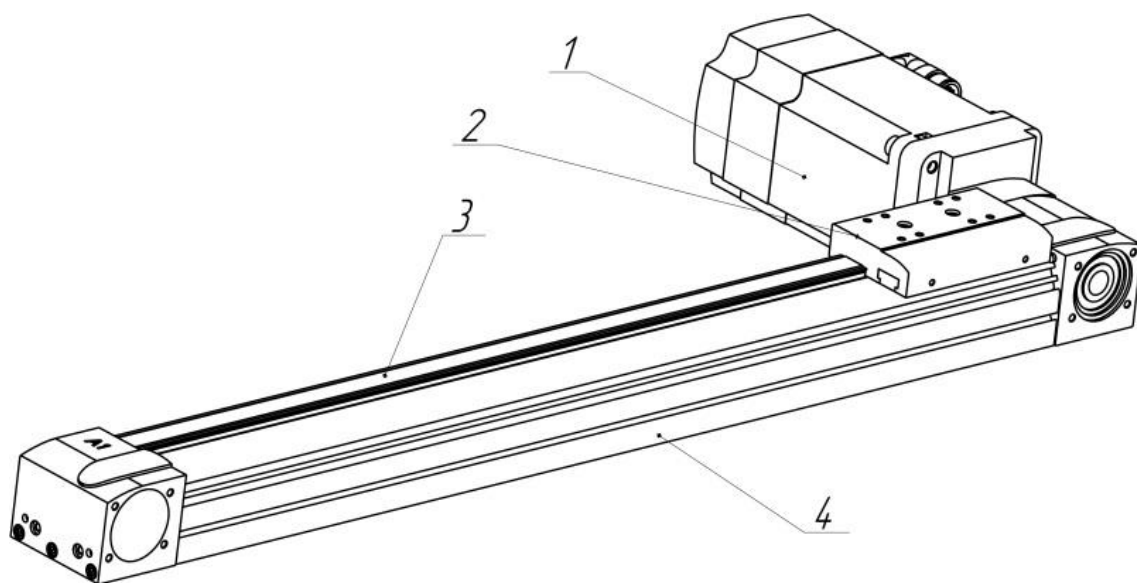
Лінійний привод із зубчастим ременем EGC-80-600-TB-KF-0H-GK:
